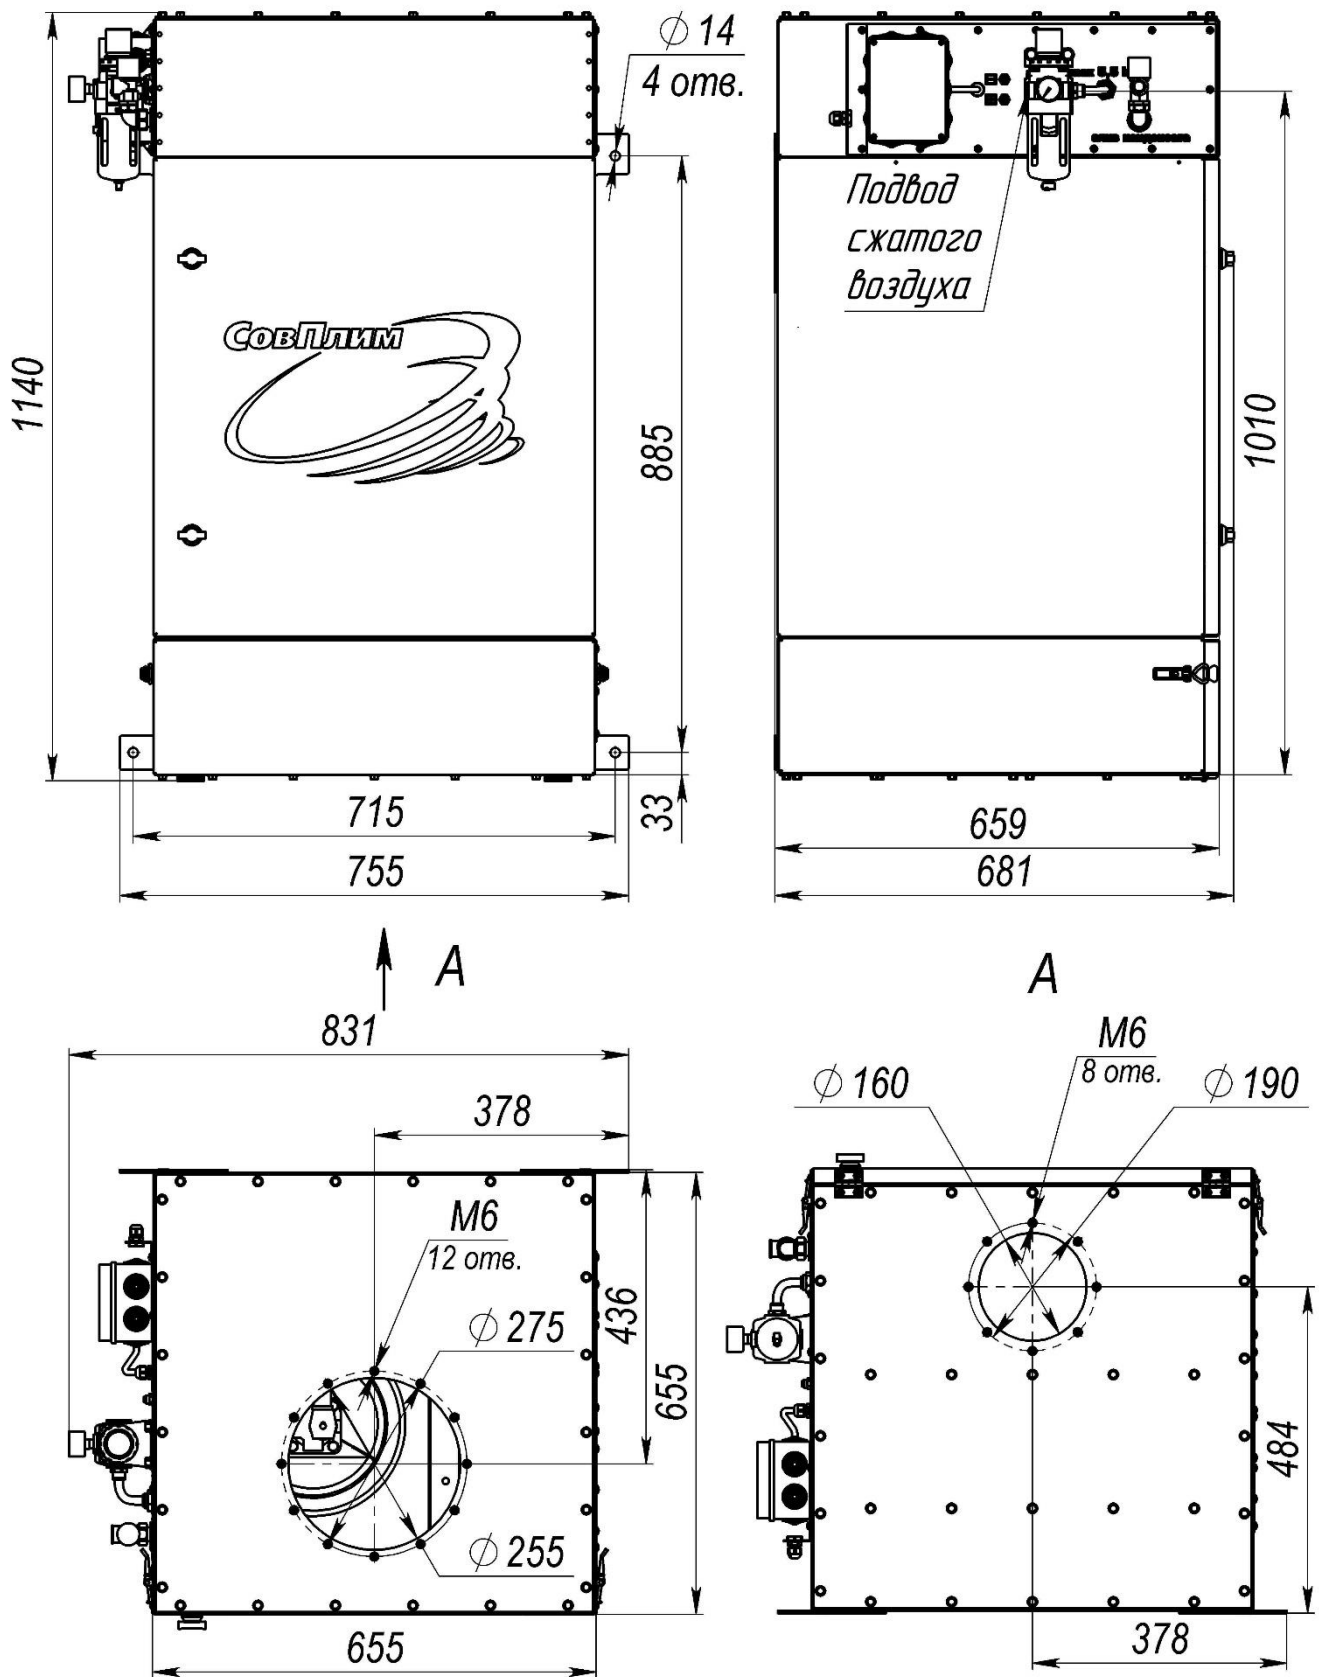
Габаритные размеры фильтра НМСФ-5
